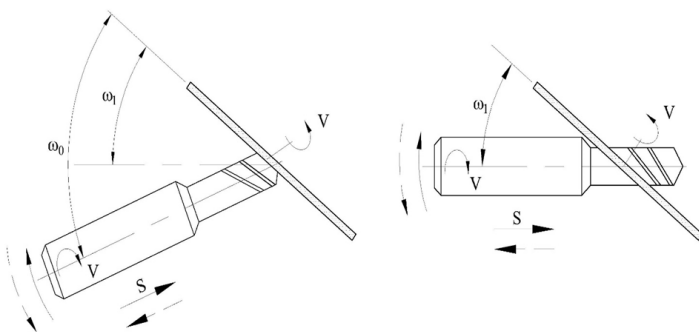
Схема изменения ориентации осей заготовки сверла и шлифовального круга методом поворота оси шпинделя заготовки.
